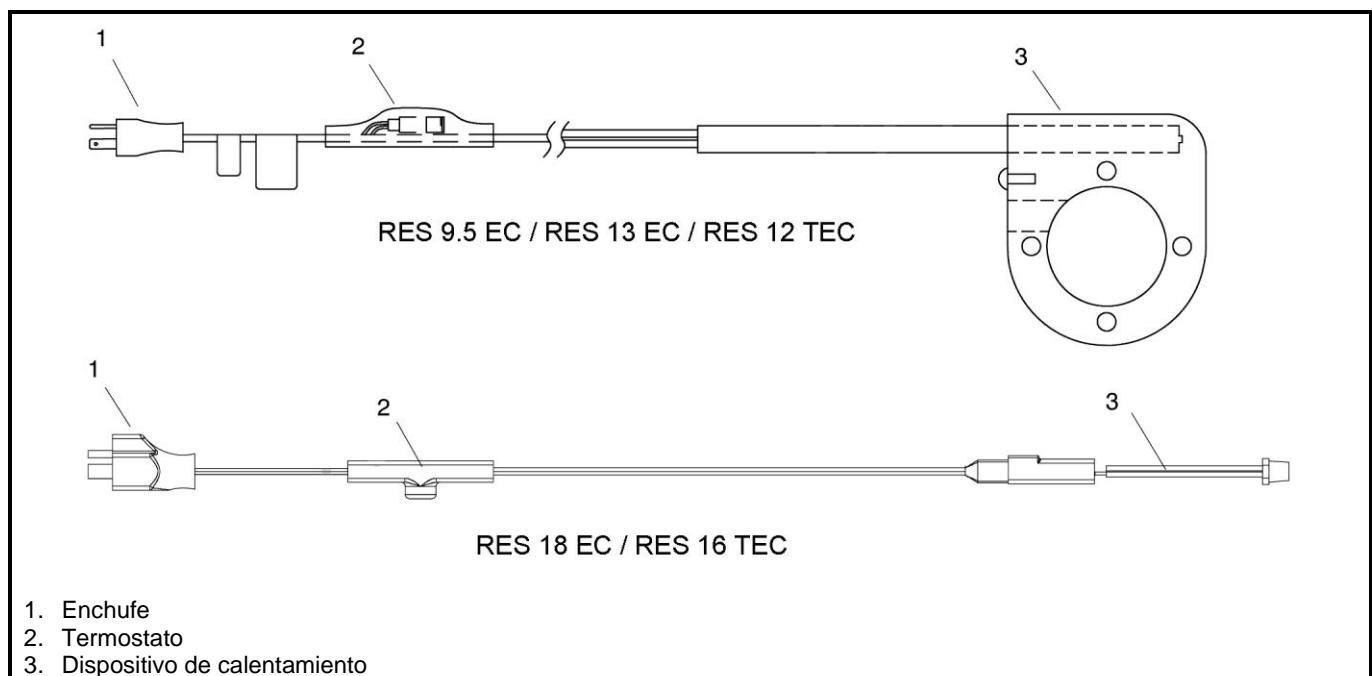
Dispositivos de calentamiento del carburador con termostato integrado
